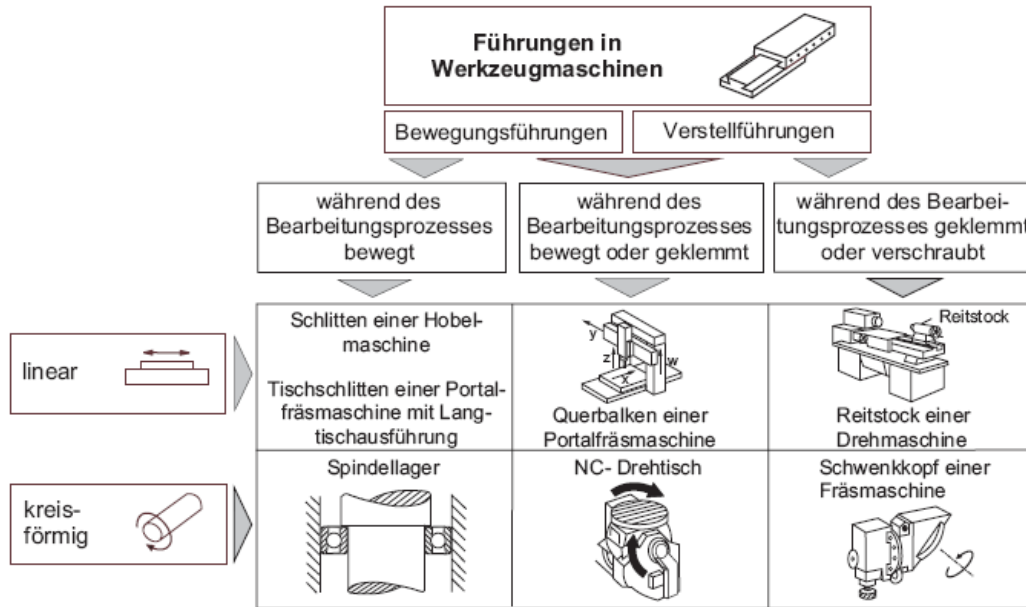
Führungen und Lagerungen in Werkzeugmaschinen [3]
